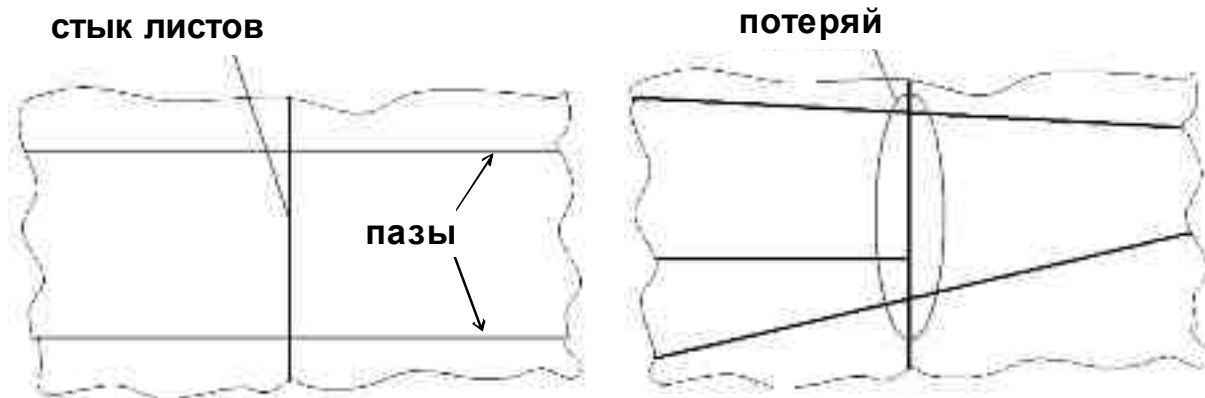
Стыки и пазы листов обшивки корпуса судна
